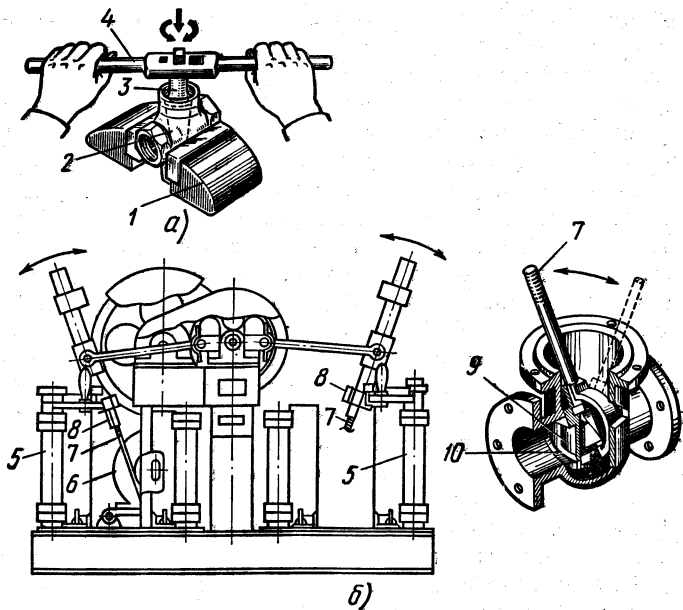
Притирка арматуры вручную (а) и на станке ВМС-42 (б): 1 — тиски, 2 — корпус, 3 — притир, 4 — вороток, 5 — зажимное устройство, 6 — электродвигатель, 7 — шток, 8 — зажим штока, 9 — диск, 10 — кольцо
